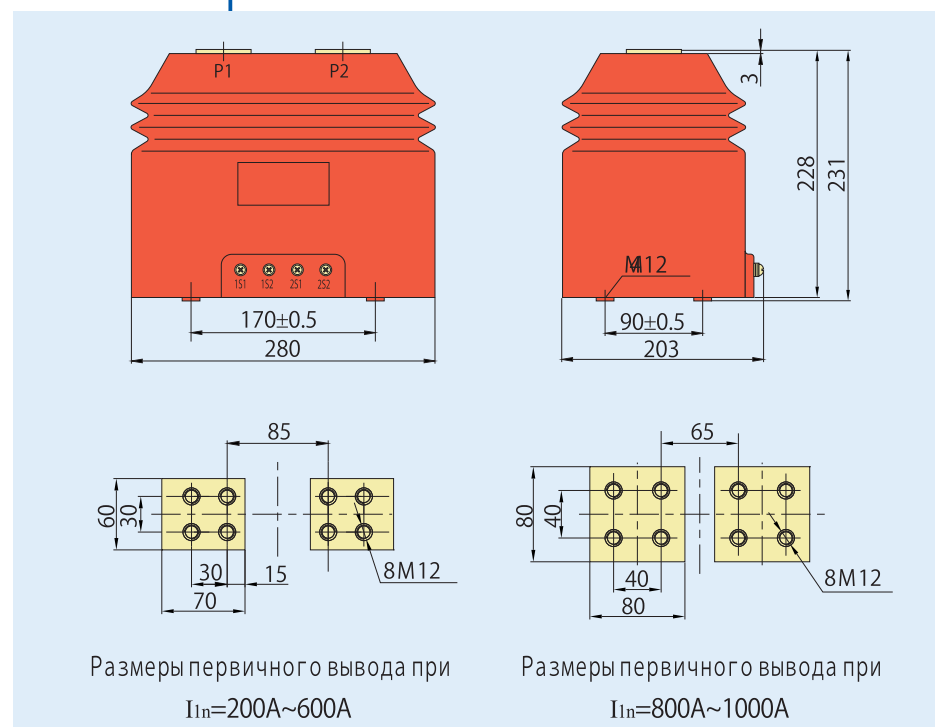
Внешний вид и размеры трансформатора тока LZZJ-10
